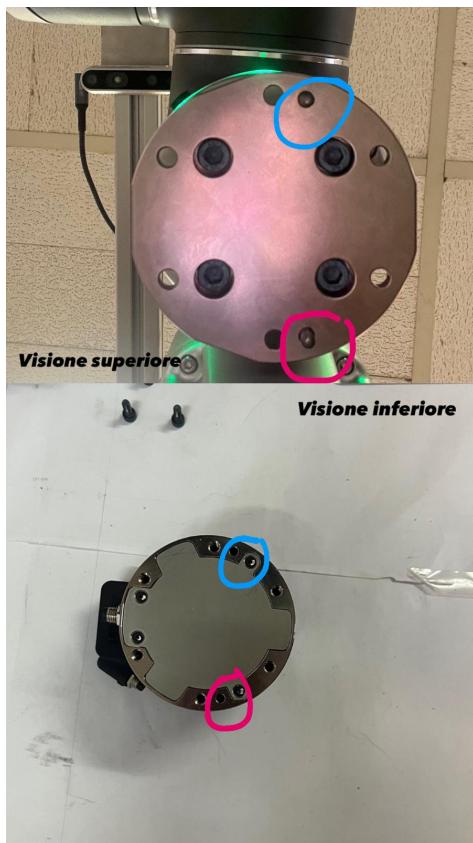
Visione superiore e inferiore per inserire il sensore di forza
